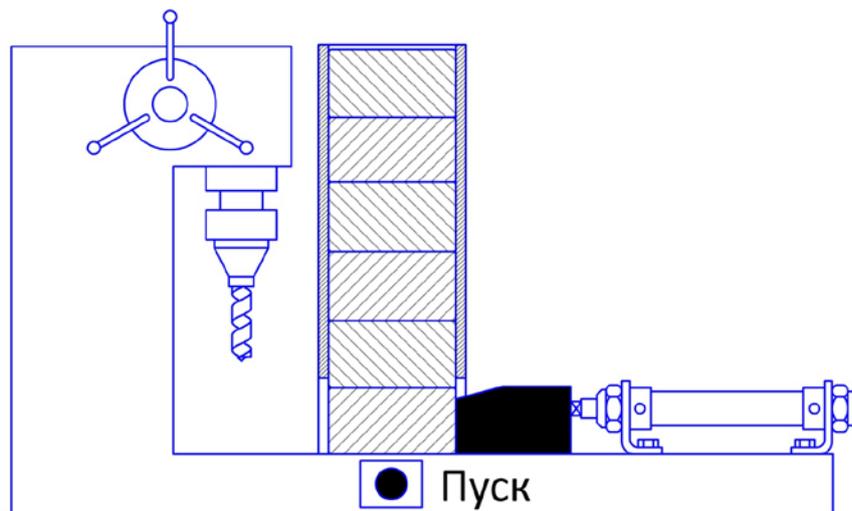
Сверлильный станок с механизированной подачей заготовок на рабочую позицию.
